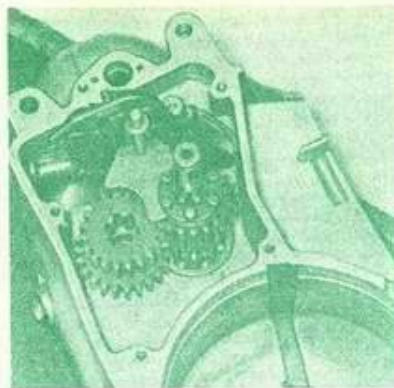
Зубчатое колесо II промежуточного вала, надетое канавкой на нижнюю вилку (на рисунке закрыта)
